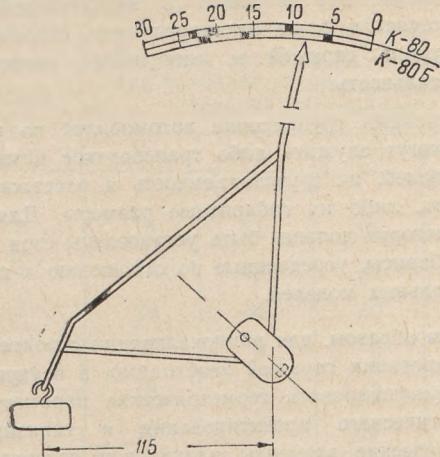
Стрелка и градуировка шкалы для настройки карбюраторов МКЗ-К80 и МКЗ-К80Б.
